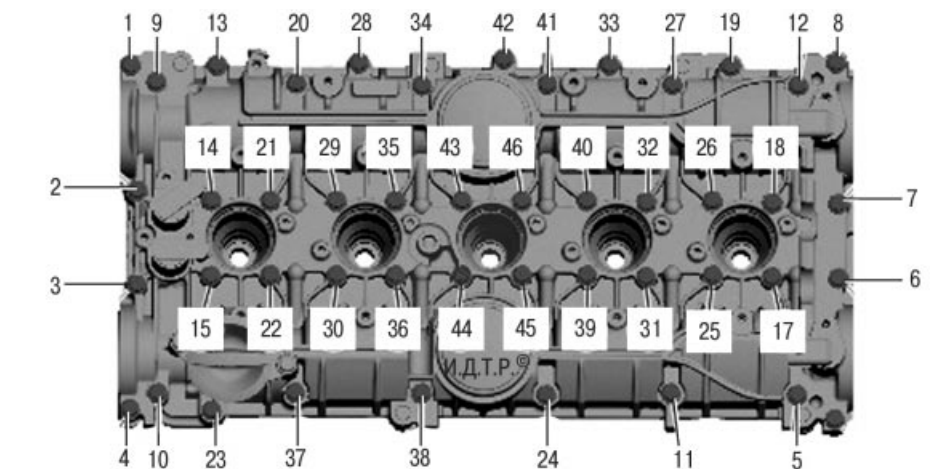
Порядок ослабления затяжки болтов крепления крышки головки блока цилиндров
